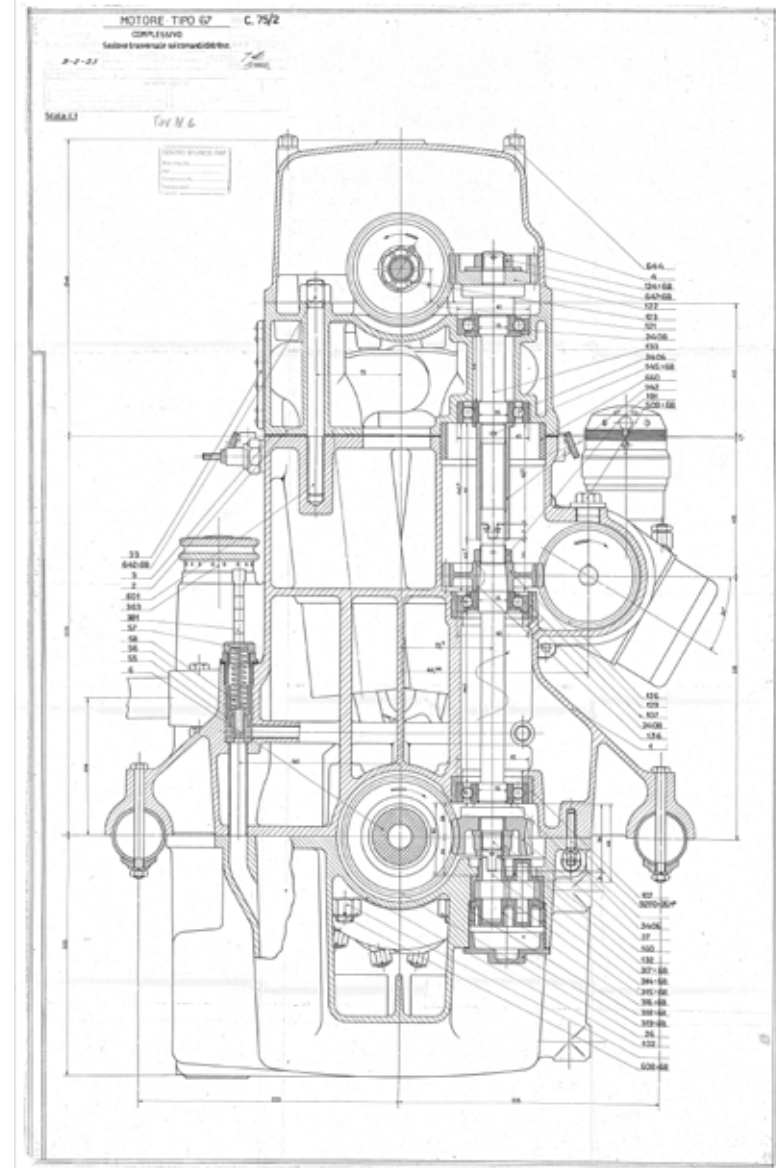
Schnittzeichnung des Motors Typ 67 für die Vor-Produktions-Lambda
